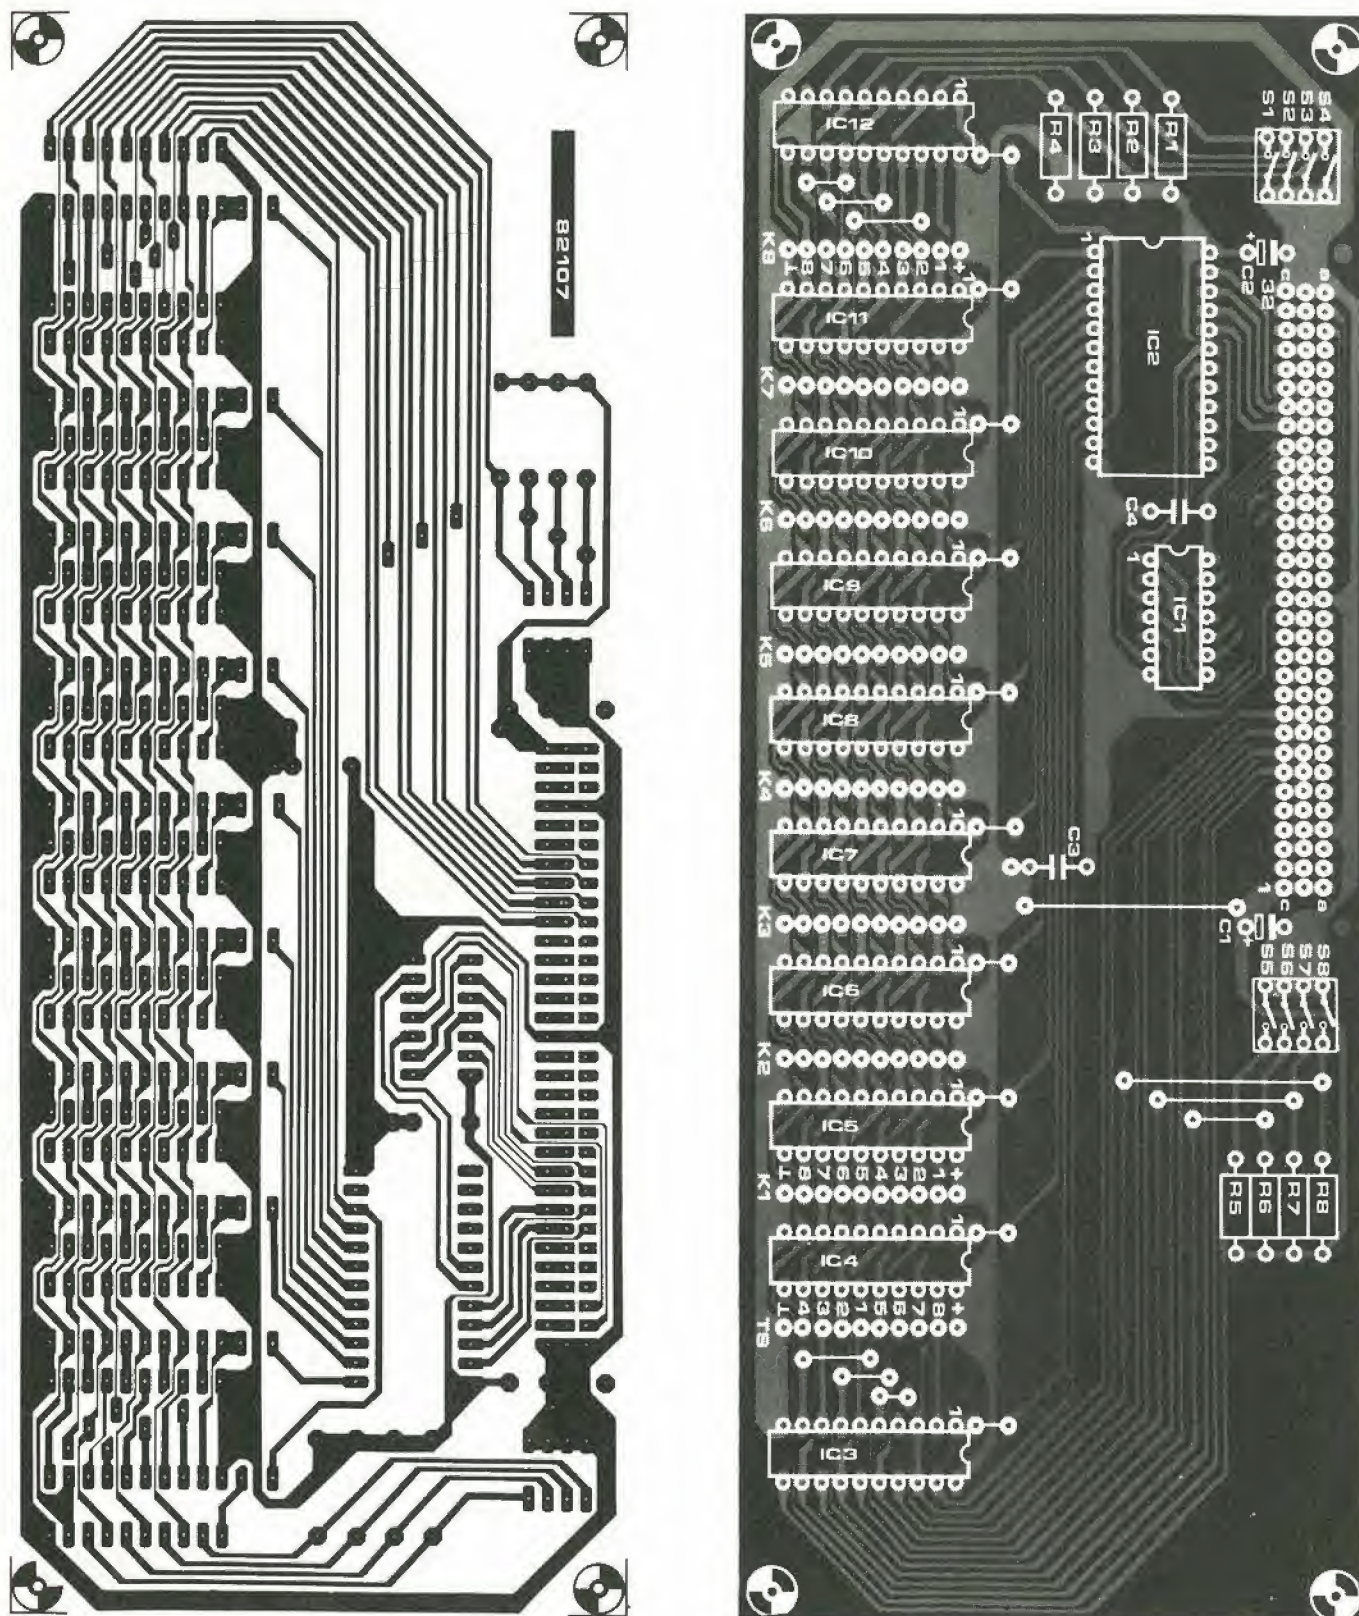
Il circuito stampato e la disposizione dei componenti del gruppo d'ingresso.
